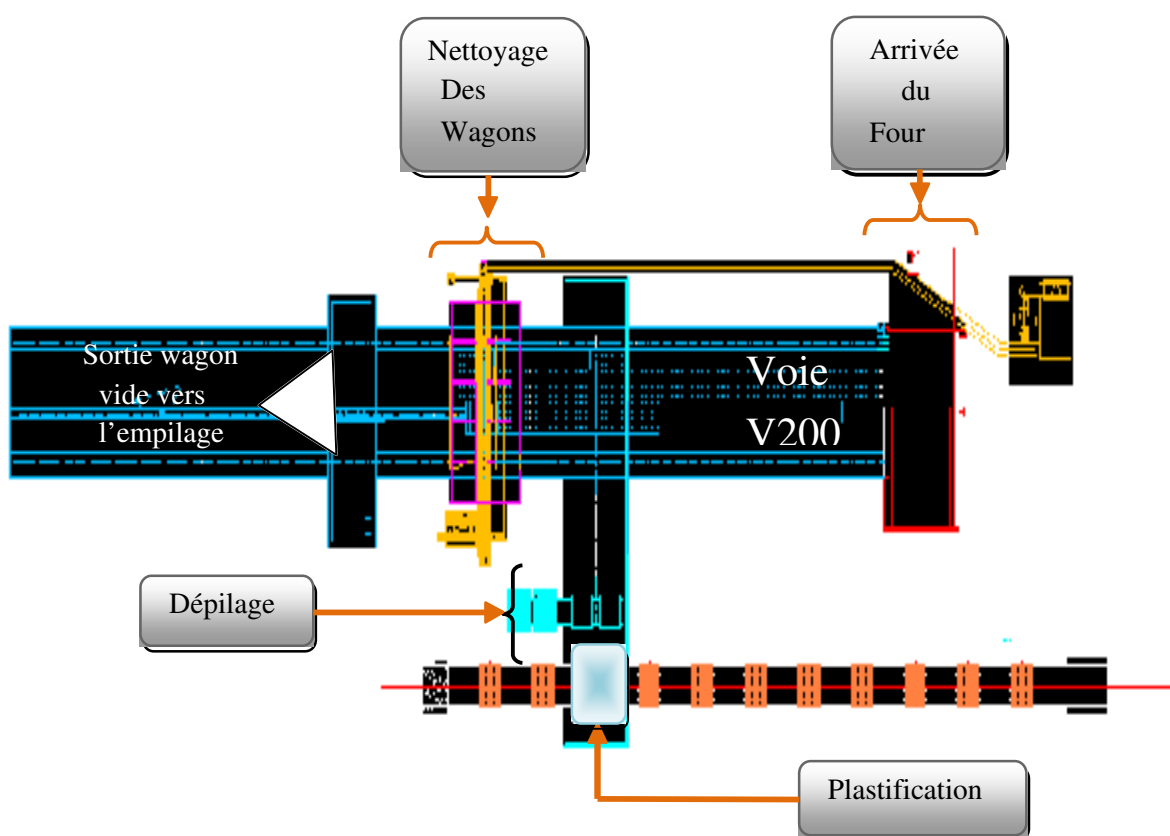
plan générale de l'atelier manutention des produits cuits (dépilage)
